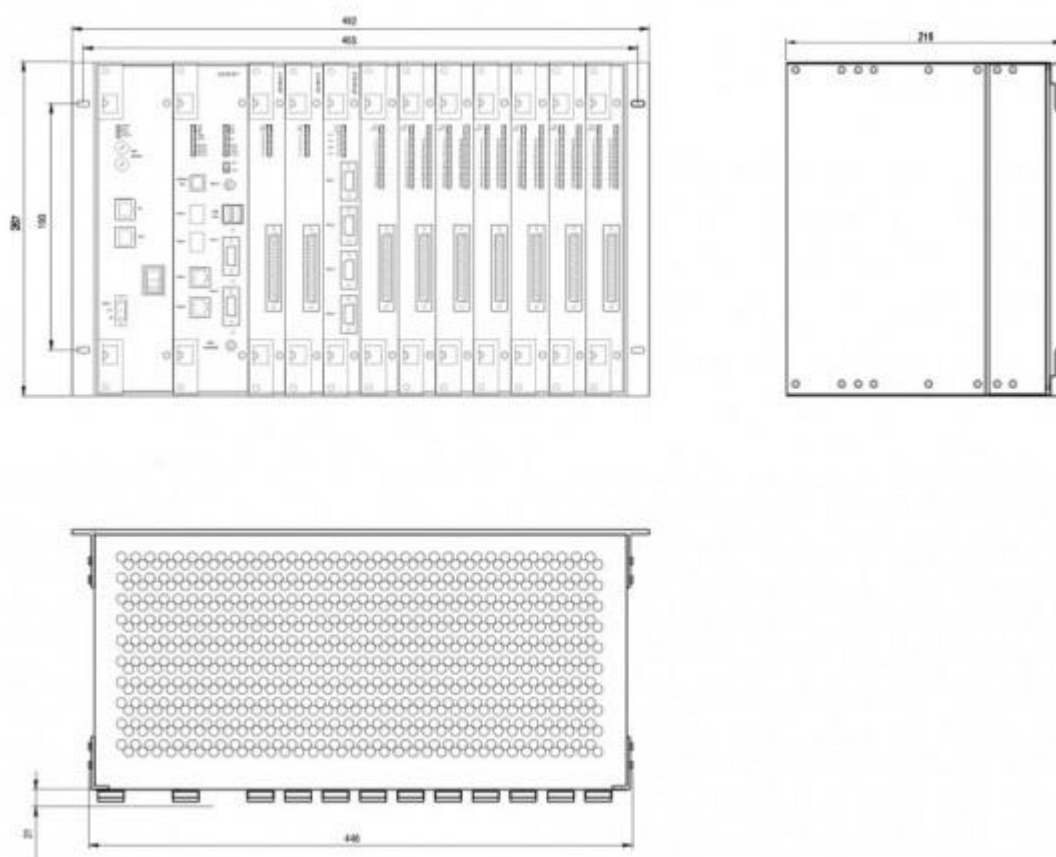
Габаритные размеры контроллера REGUL-R600
